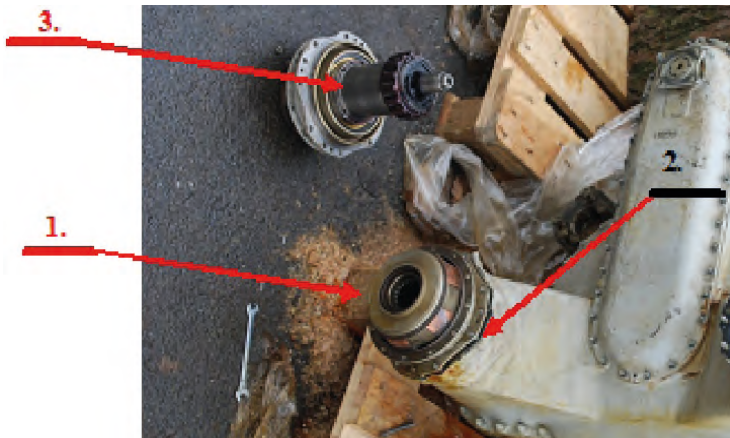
Wejście wielowypustowe do pólki sprzęgła jednokierunkowego w przekładni głównej WR-24: 1 – wielowypust wewnętrzny; 2 – odlew korpusu sprzęgła jednokierunkowego
